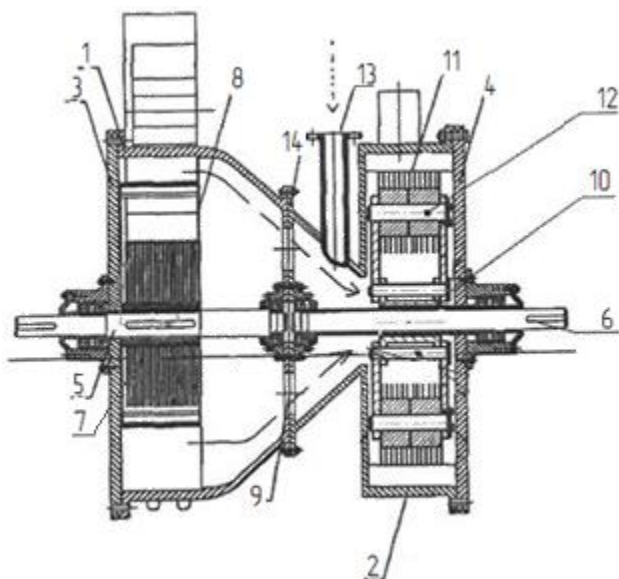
РЦА КД: 1 – камера дробления, 2 – камера тонкого помола; 3, 4 – крышка; 5, 6 – вал; 7 – ротор камеры дробления; 8 – перегородка камеры дробления; 9 – переходное отверстие; 10 – ступица; 11 – щетка; 12 – ось; 13 – патрубок добавок; 14 – межкамерная перегородка
